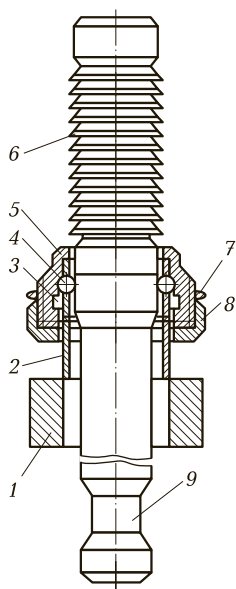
Устройство для запрессовки втулок и одновременной обработки отверстия:
